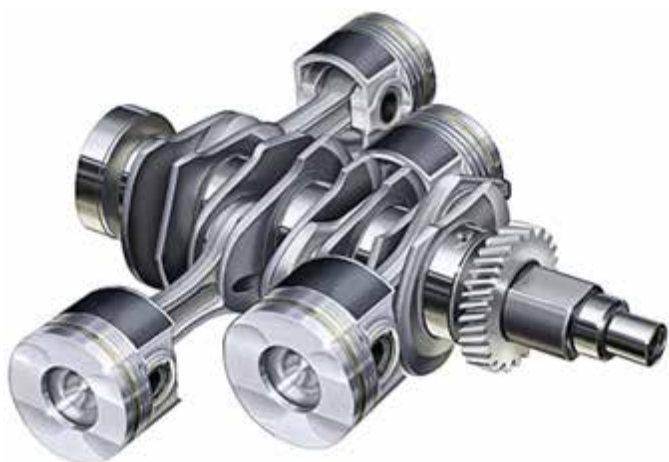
Хотя коленчатый вал оппозитного двигателя похож на коленчатый вал R-4, поршни в цилиндрах двигателя не совершают попарных движений; источник: Subaru
